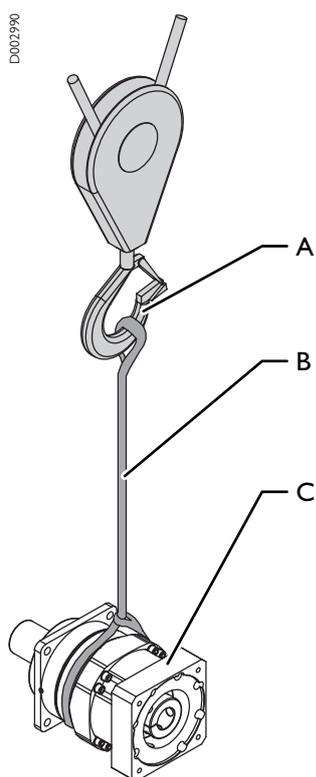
Зачалить такелаж: Планетарный редуктор
